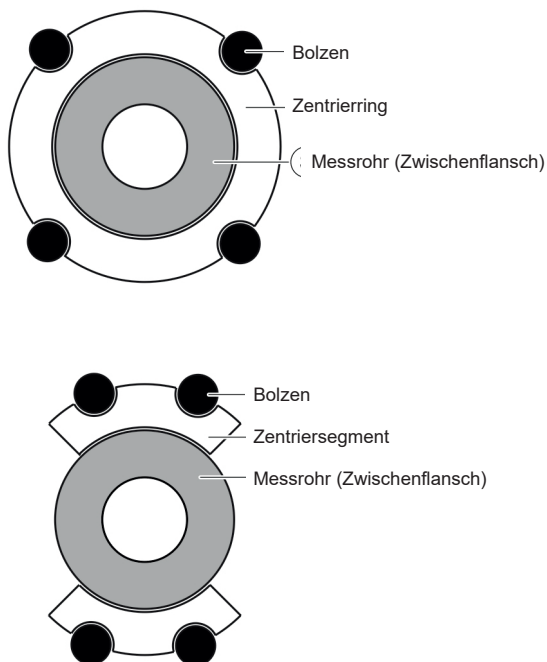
Zentrierung der Zwischenflanschausführung mit Ring bzw. Segment
